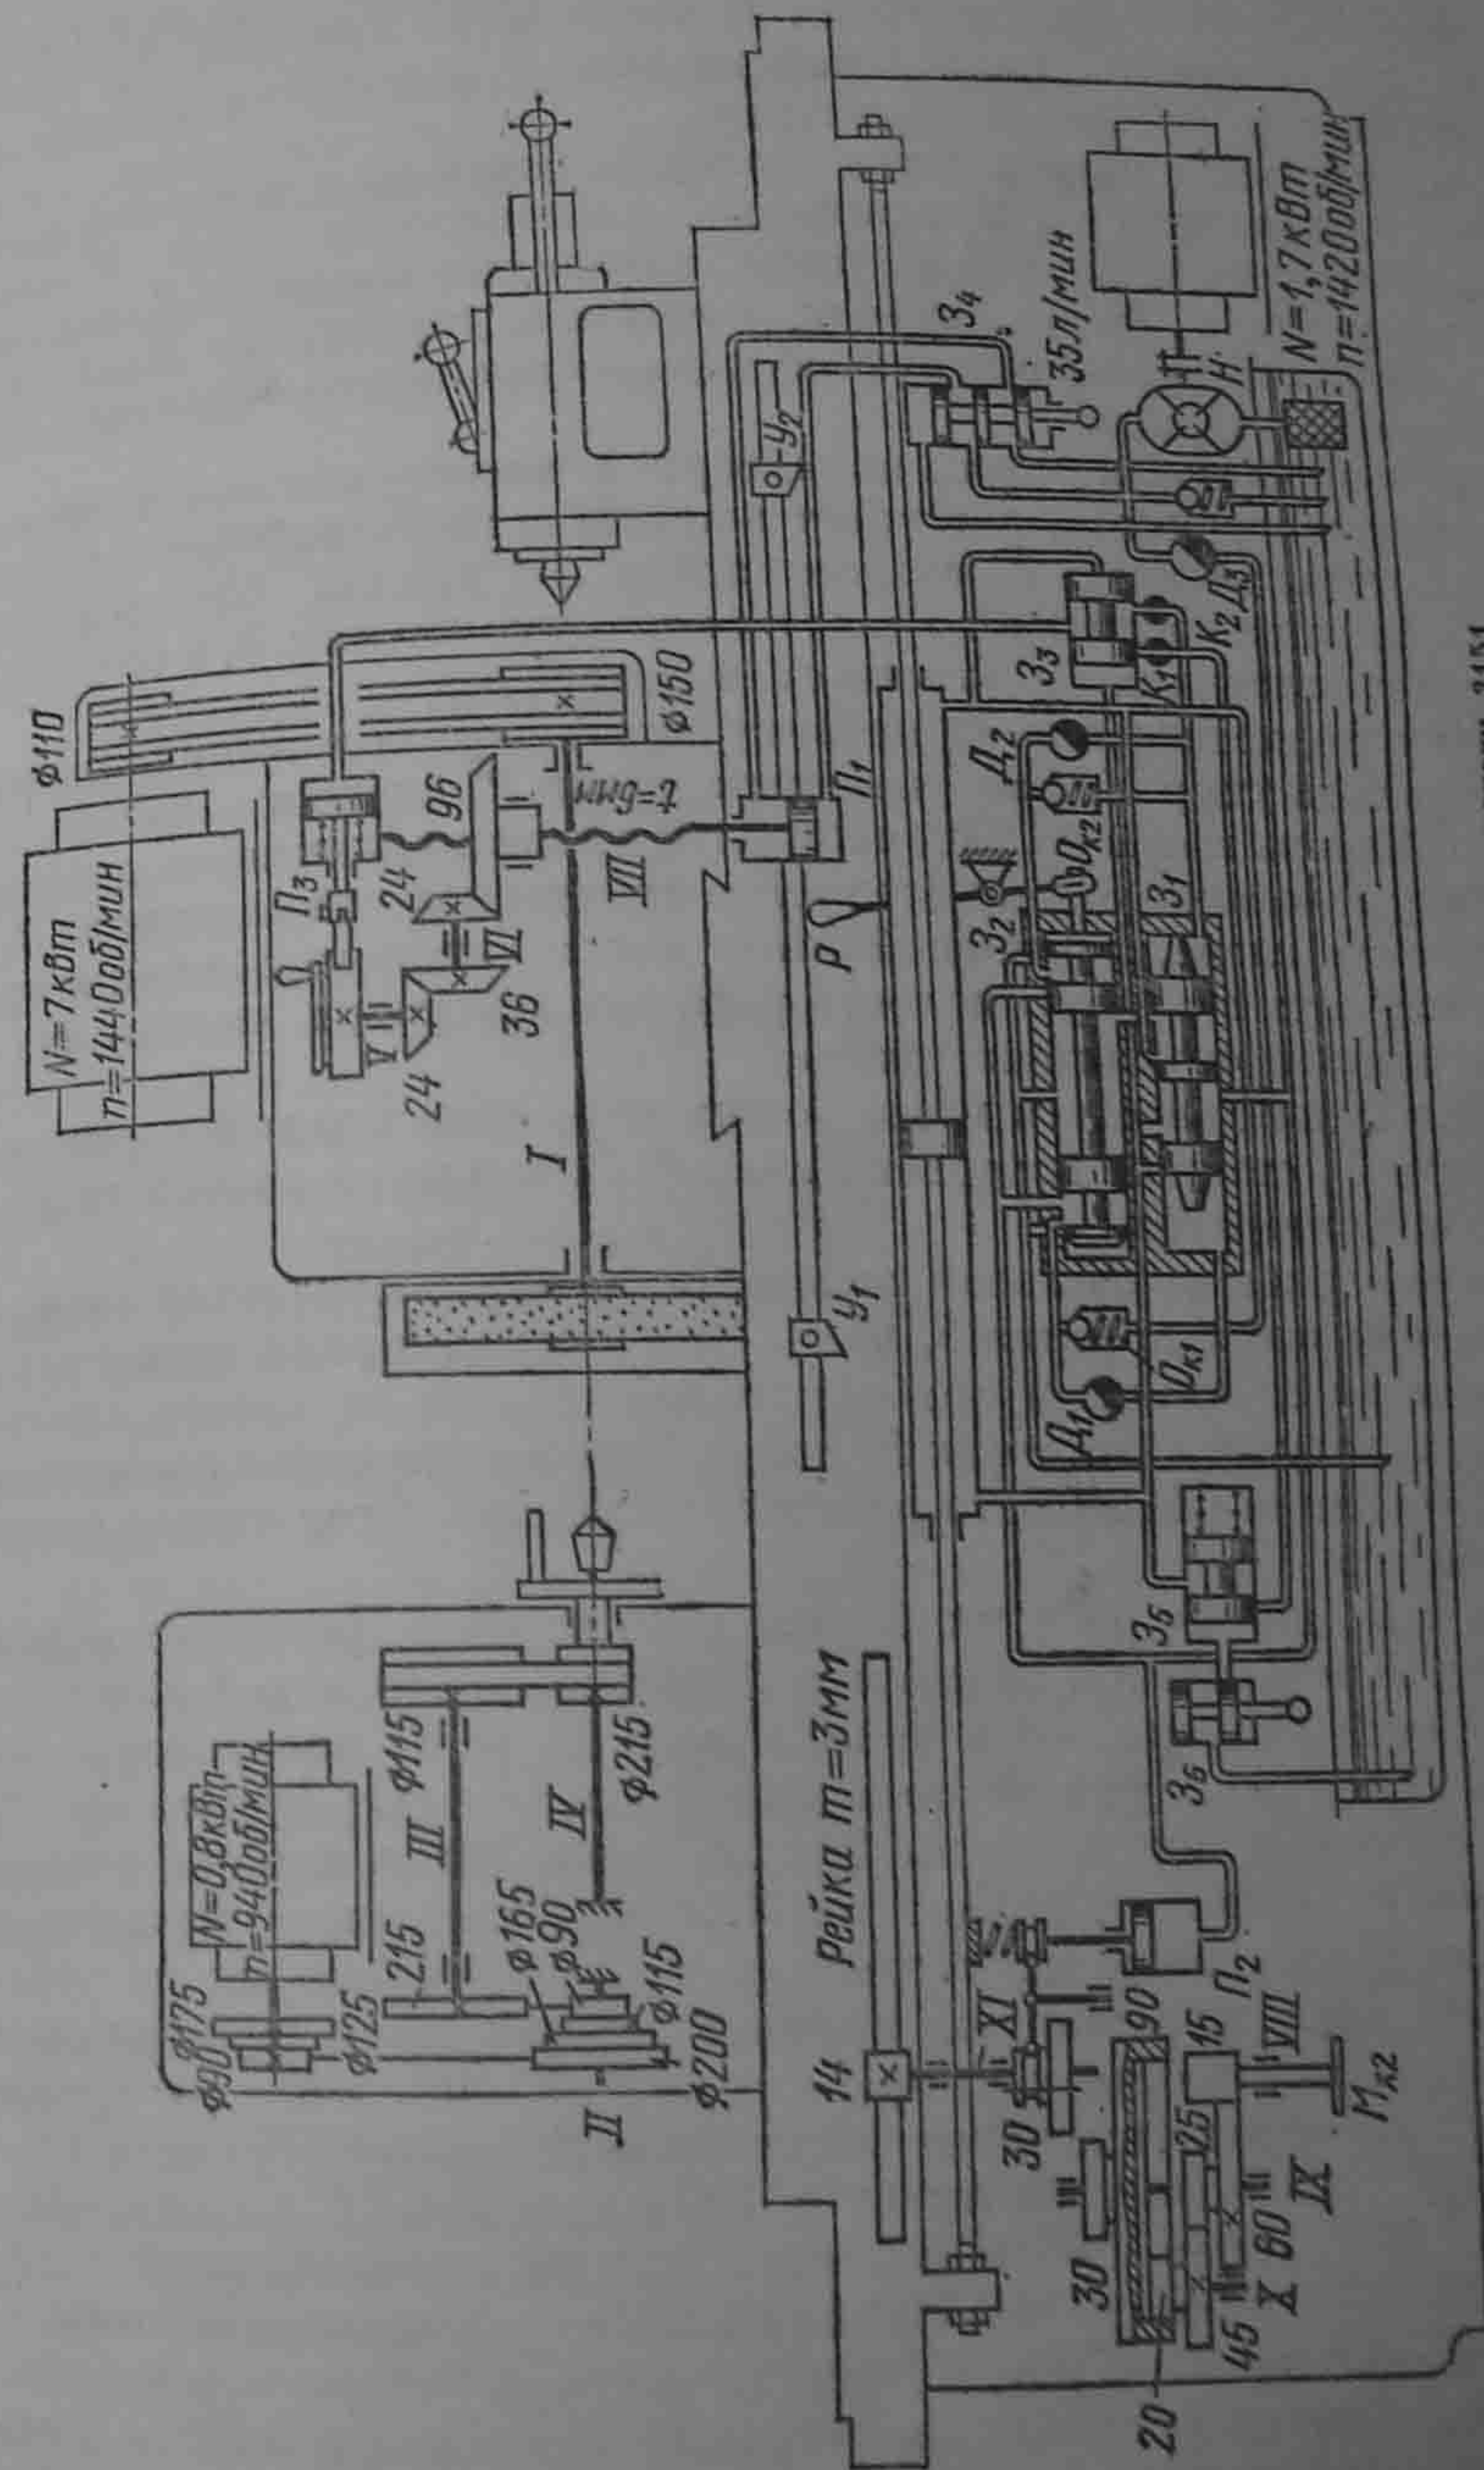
Кинематическая и гидравлическая схемы круглошлифовального станка модели 3151
